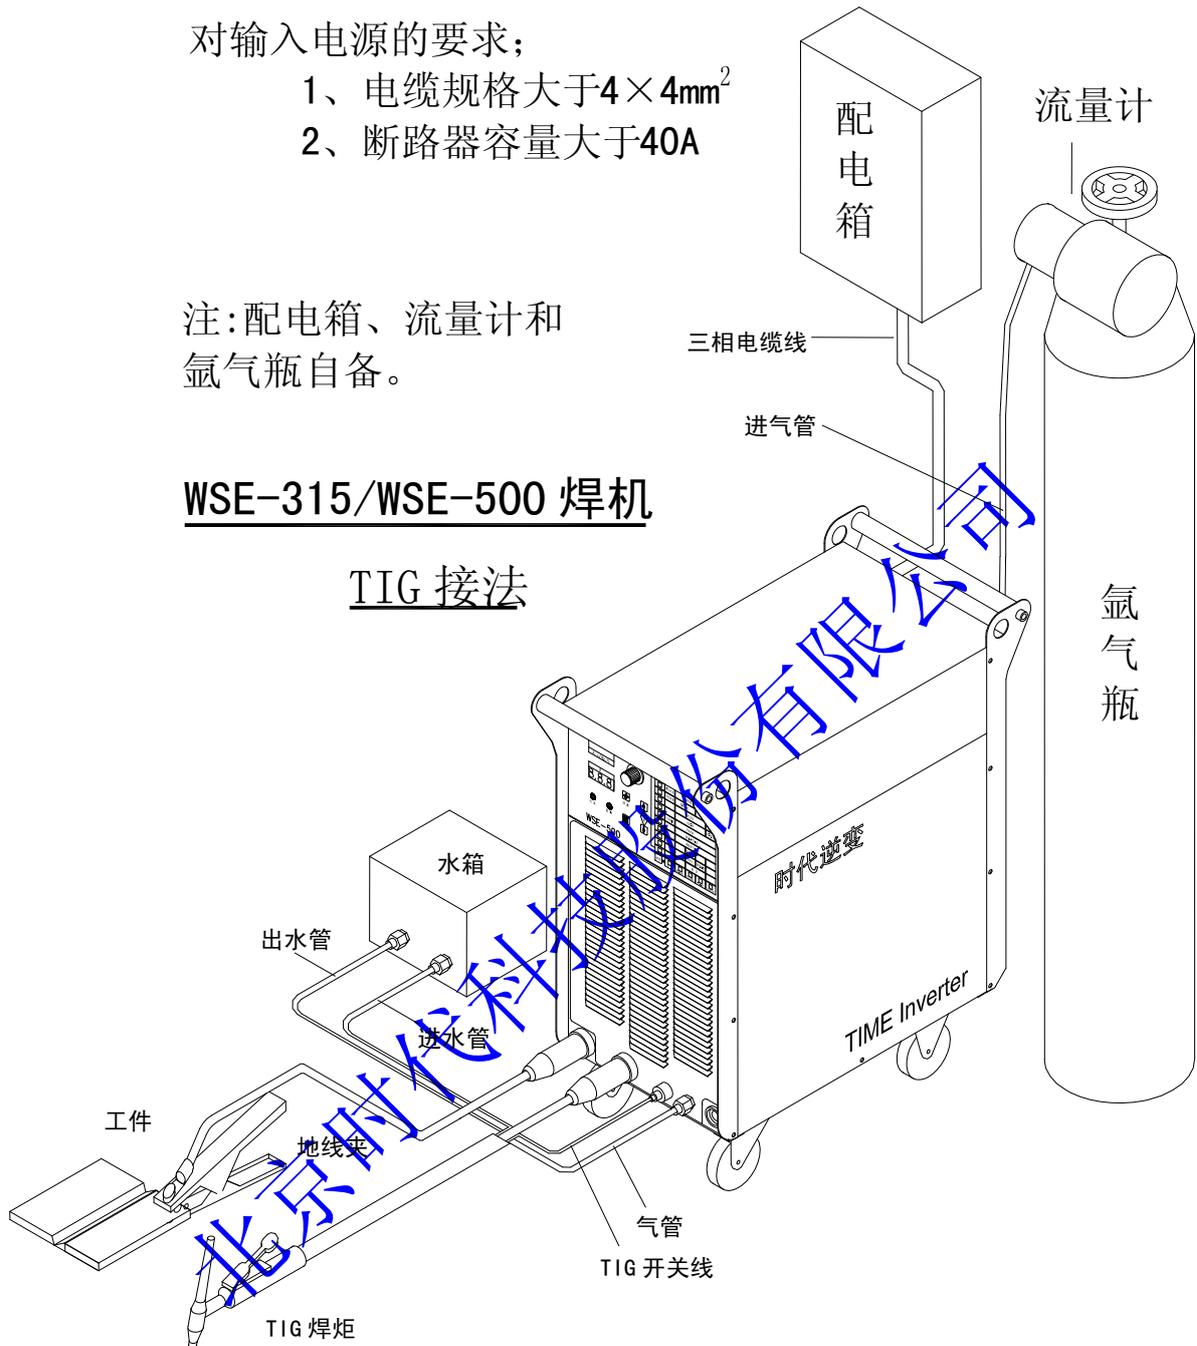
C WSE-315/WSE-500 焊机的 TIG 接法
